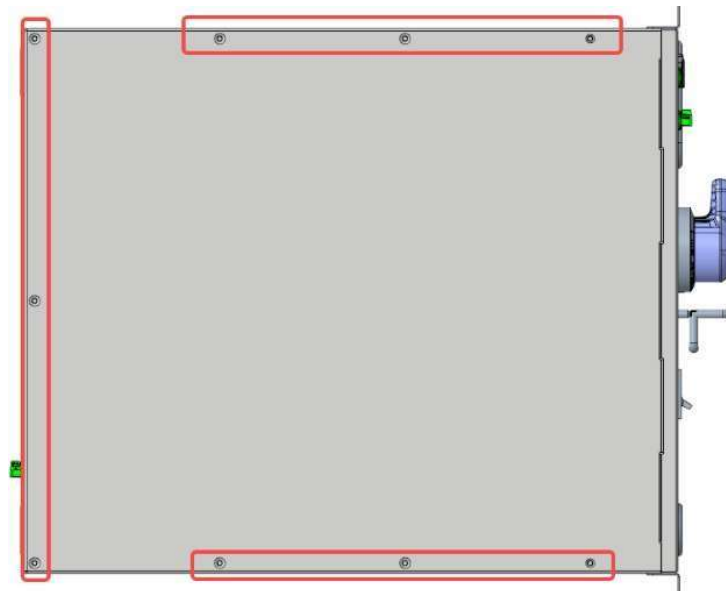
Retire los tornillos de fijación de la placa de cubierta de la caja de distribución
